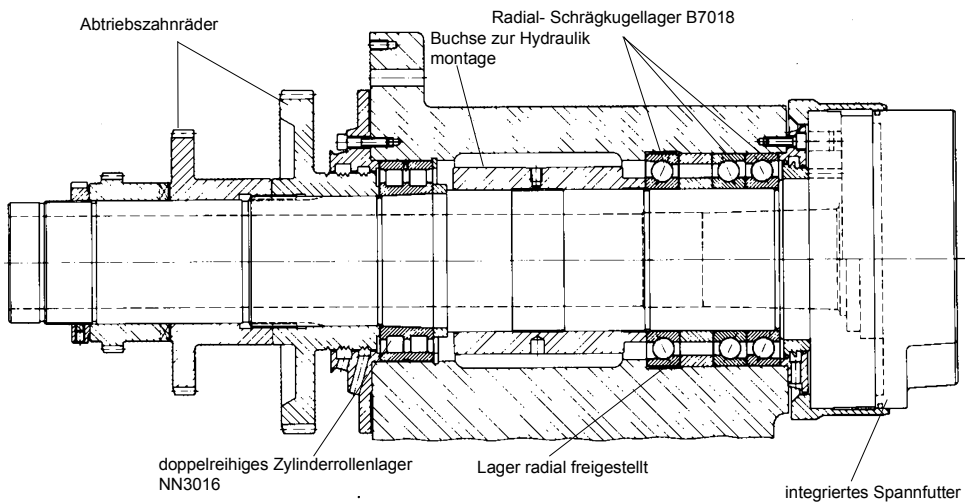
Arbeitsspindel als Werkzeugspindel zum Fräsen, Bohren u. a. für ein CNC-Bearbeitungszentrum. (Quelle: nach FAG)
